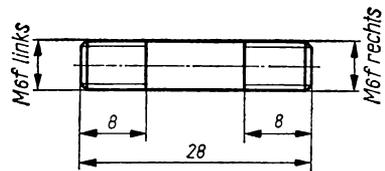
Gewindeteil mit Rechts- und Linksgewinde
